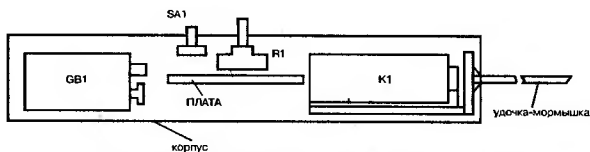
Примерное расположение деталей в корпусе ручки
